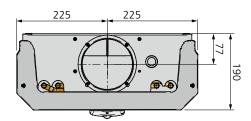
Dimensions ADRIATIC AWC Prisma, vue arrière du raccordement aéraulique
